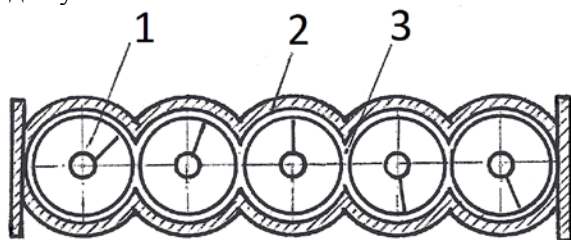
Поперечный разрез прессы: 1 – винт; 2 – кожух; 3 – пресскамера
